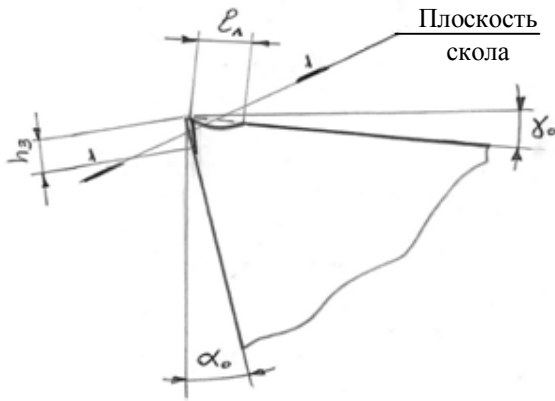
Схема образования фаски и лунки износа, приводящие к сколам режущей кромки инструмента
